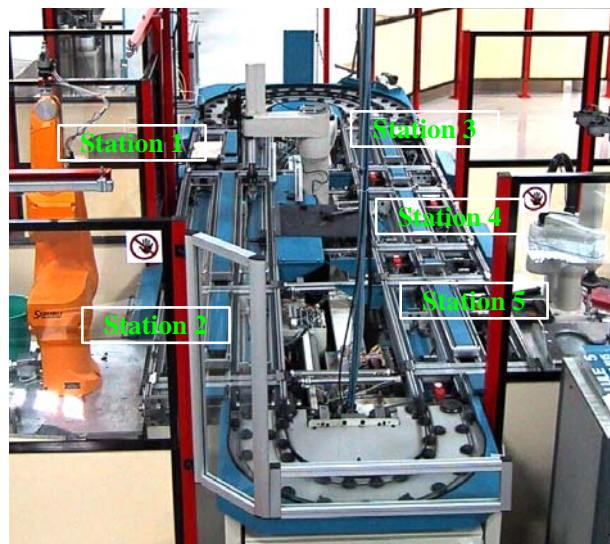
Vue d'ensemble de la plate-forme flexible du LAB
